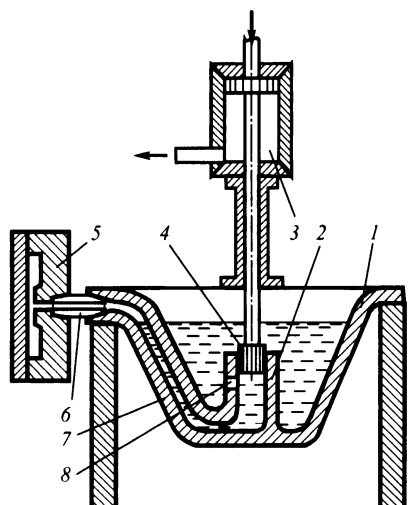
Схема литейной машины с горячей камерой прессования
